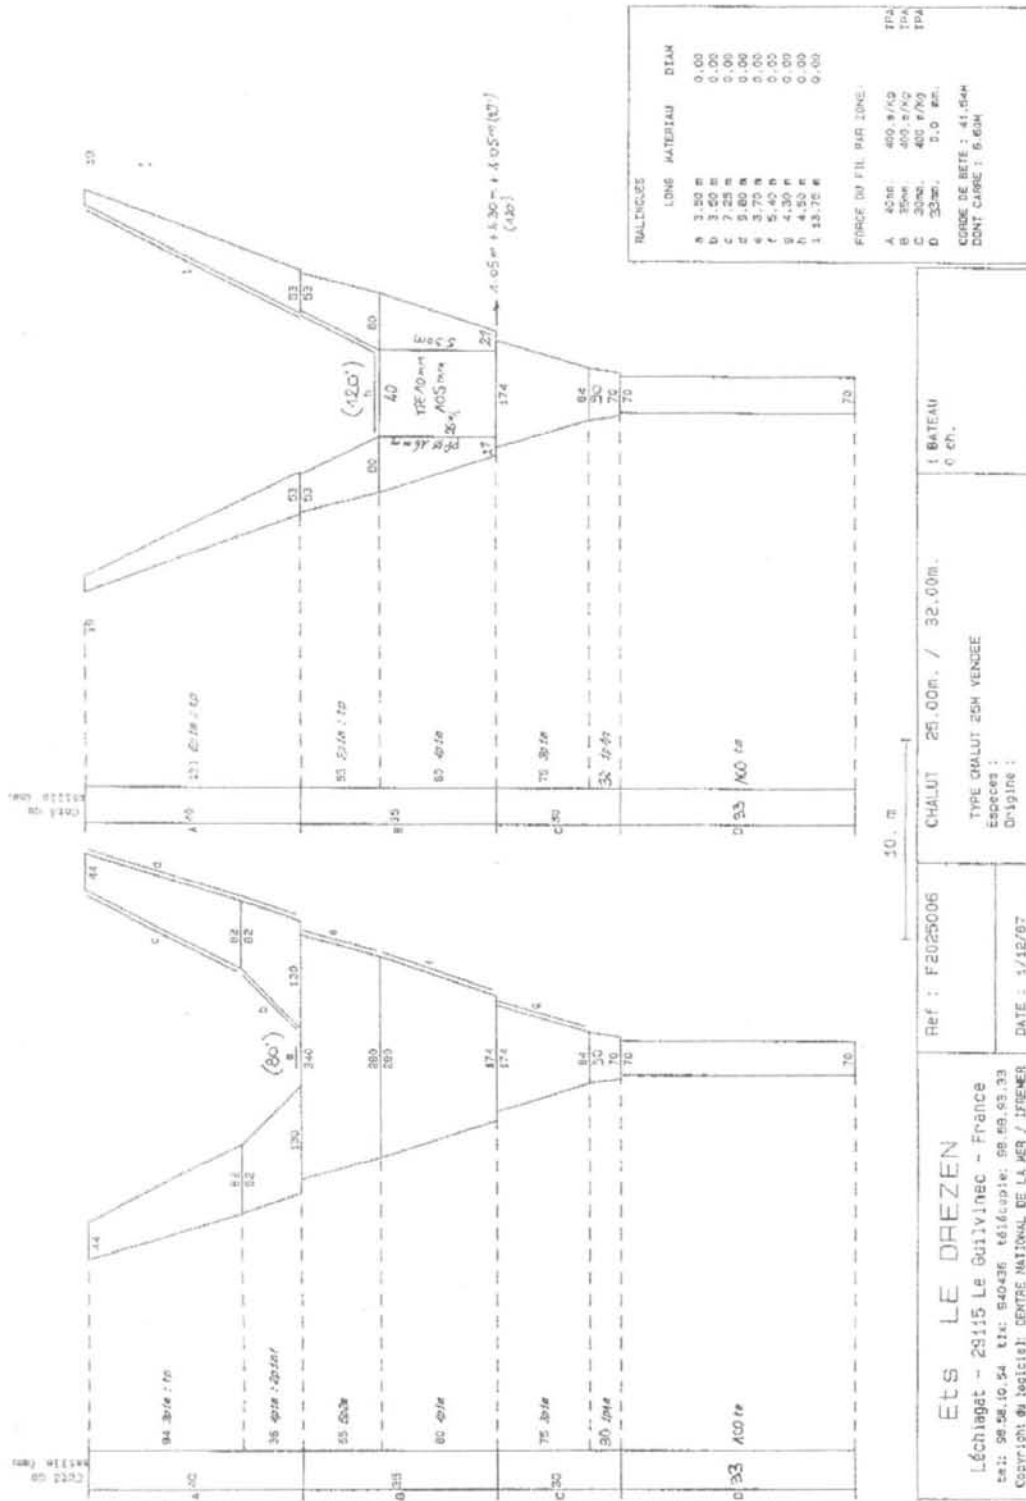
Plan du 25 m à grille (plan Le Drézen F2025006).
